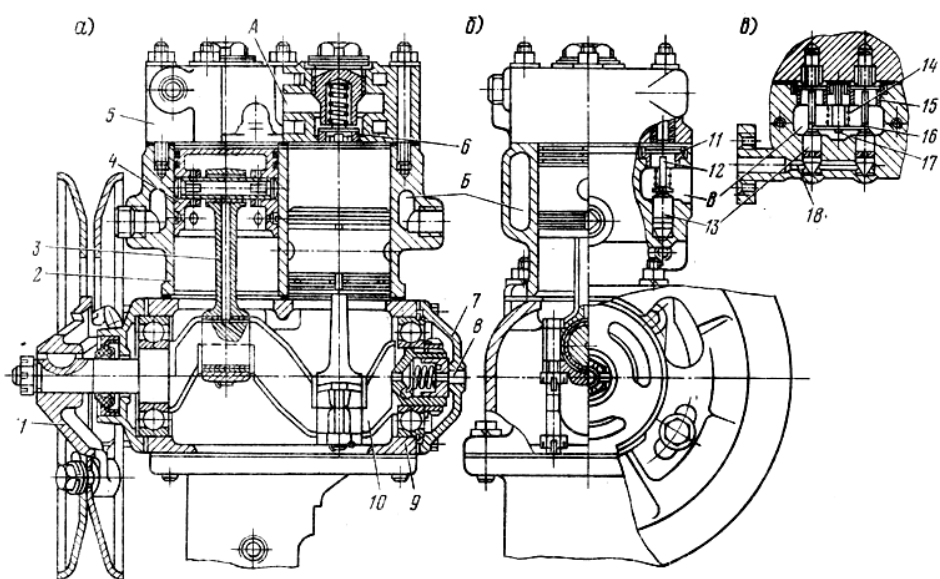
Компрессор пневматического привода тормозов автомобиля ЗИЛ-130
